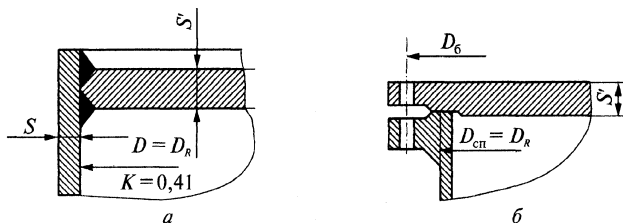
Типы крепления крышки к корпусу аппарата:
